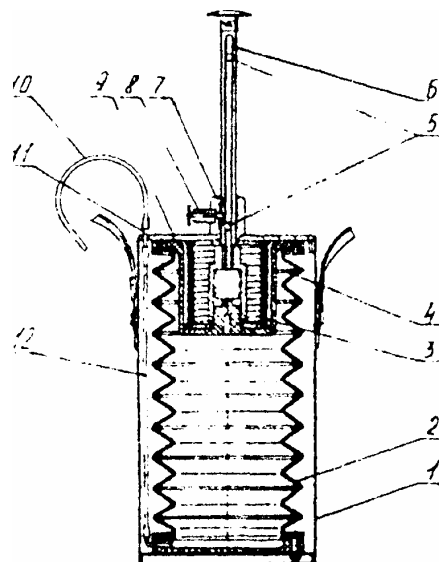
Повітрязбірний пристрій УГ-2: – корпус; 2 – сифон; 3 – пружина; 4 – кільце розпирне; 5 – канавка з двома поглибленнями; 6 – шток; 7 – втулка; 8 – фіксатор; 9 – плата; 10, 12 – трубка гумова; 11 – штуцер
